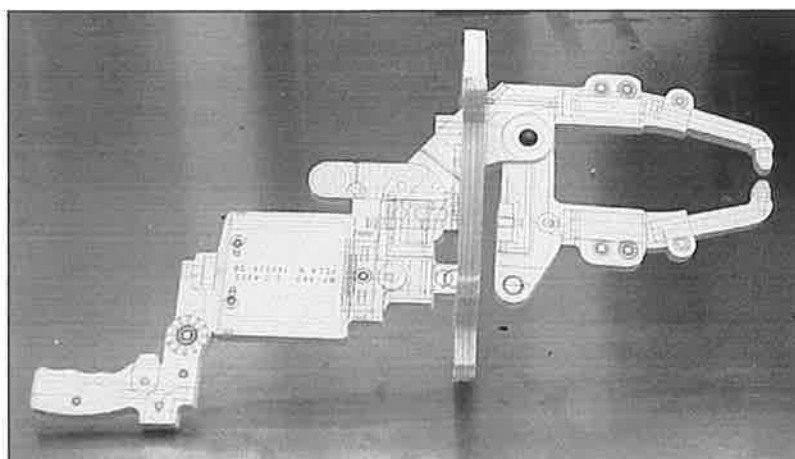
Mock-up em papelão de uma pinça de solda. (Macarrão, 2004).
